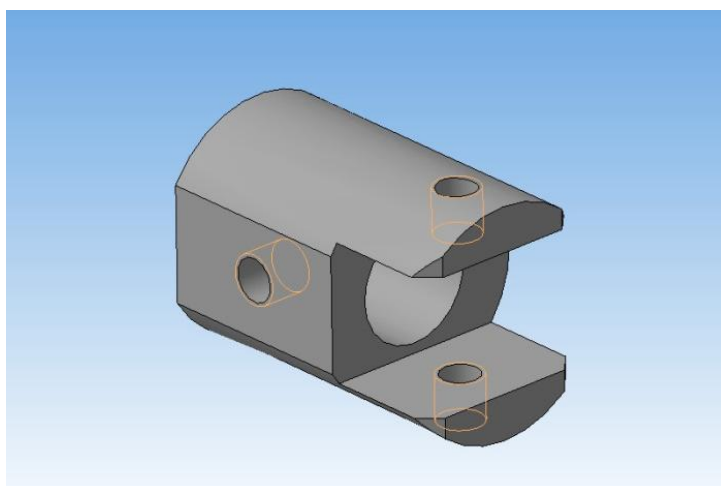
3D модель корпуса подвижной опоры
